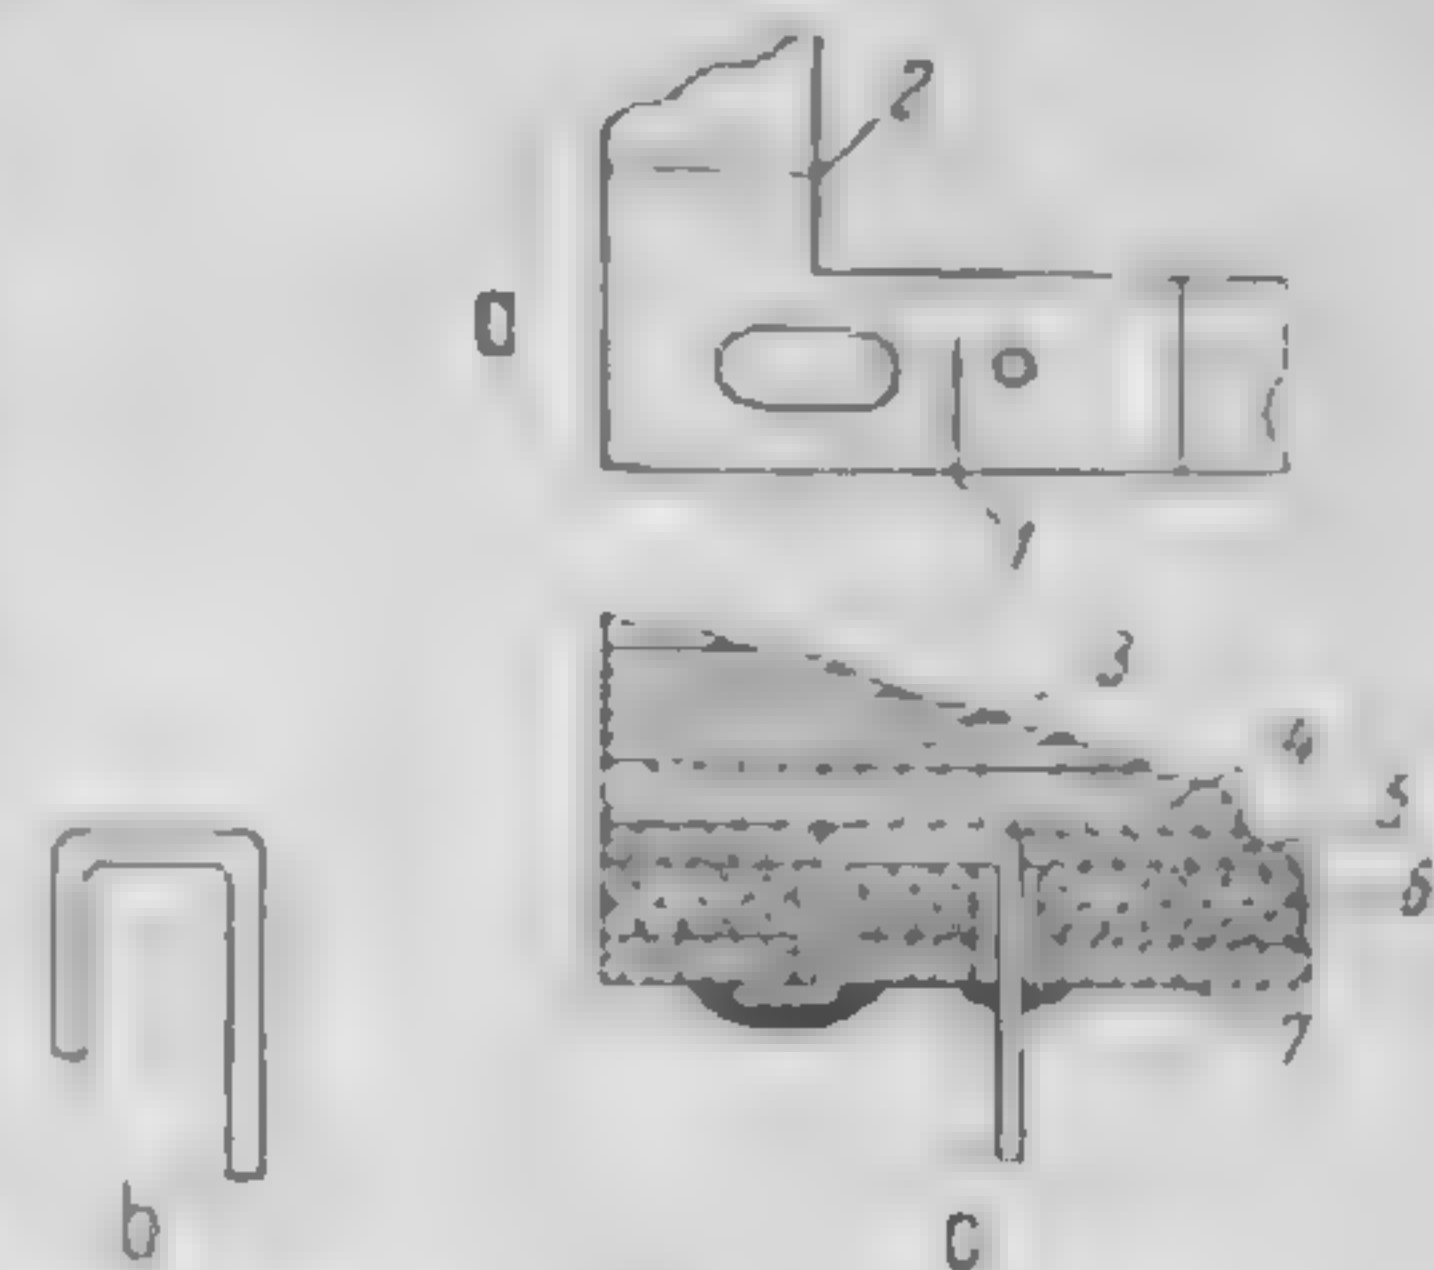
Transformator armat pentru fixarea pe placa imprimată:
